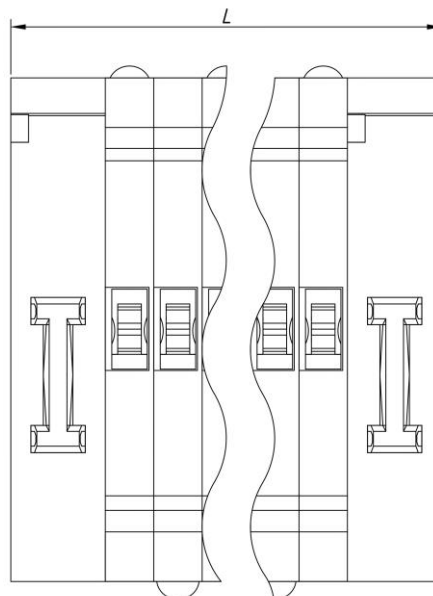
Общий вид тестовой крышки ЭПТК. Вид сзади.
